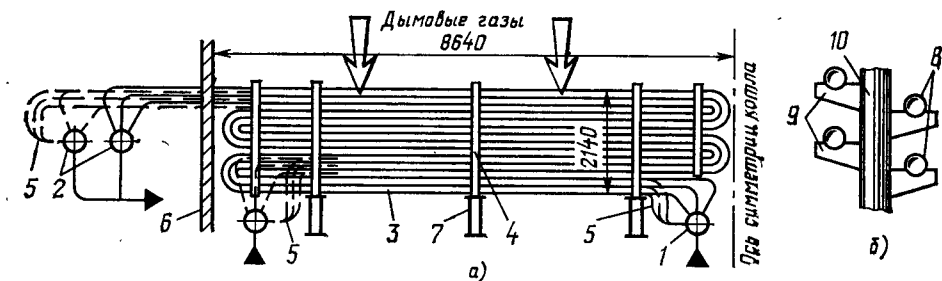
Крепление конвективного трубного пакета с горизонтальными змеевиками. а — с опиранием на вертикальные стойки и охлаждаемые опорные балки; б — с опиранием на планки, приваренные к вертикальным подвесным трубам; 1 — входной коллектор; 2 — выходной коллектор; 3 — трубный пакет; 4 — дистанционирующая стойка; 5 — включение в коллектор крайних змеевиков трубного пакета; 6 — боковая стена газохода; 7 — опорная балка, охлаждаемая воздухом; 8 — трубы змеевиков; 9 — опорные планки; 10 — подвешивающая труба.
